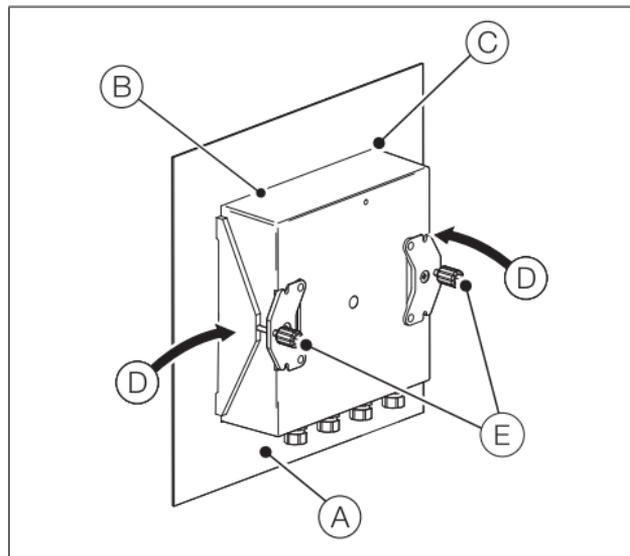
Dettagli di montaggio – Indicatore CMF160
